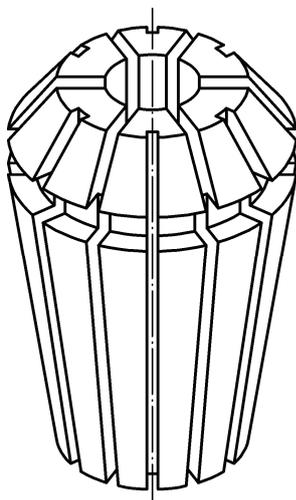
Spanneinsatz (Spannzange) für Schaftwerkzeuge
